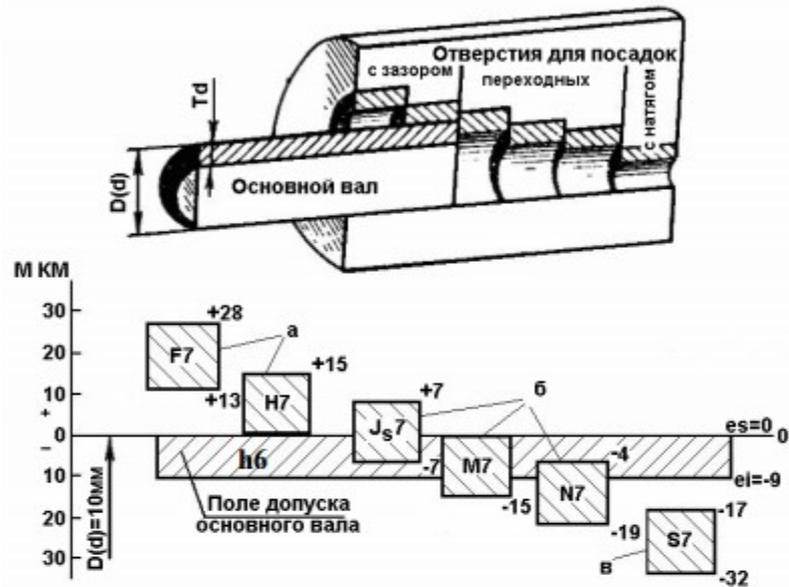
Расположение полей допусков основного вала “h” и отверстий в системе вала для посадок:
